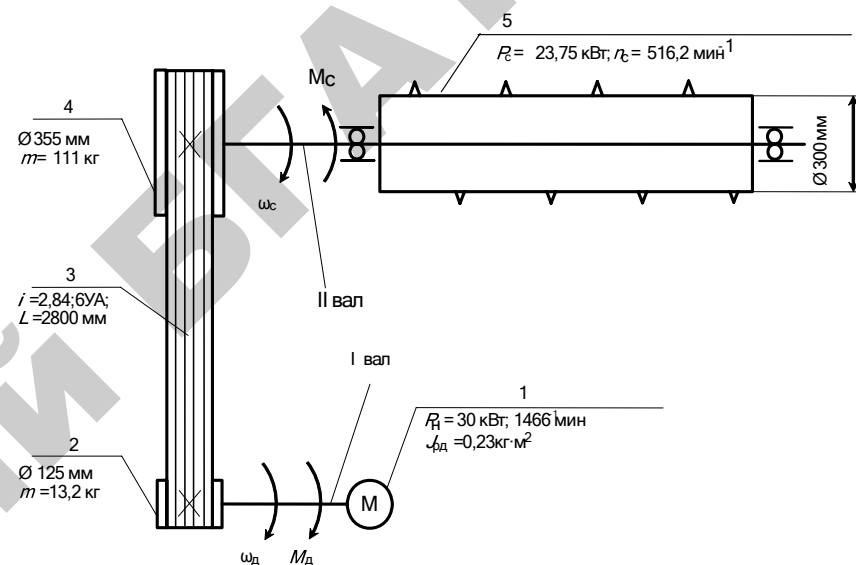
Образец кинематической схемы шнекового смесителя
